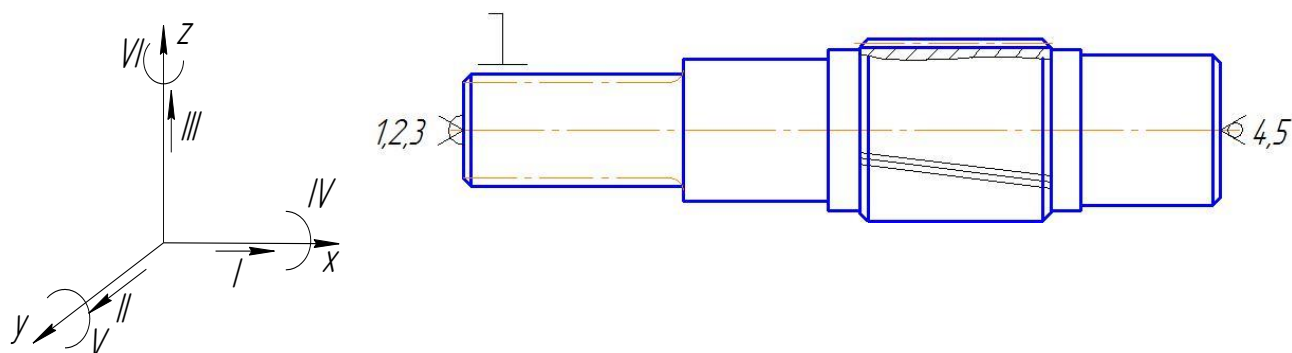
Ескіз обробки заготовки на операції 050
